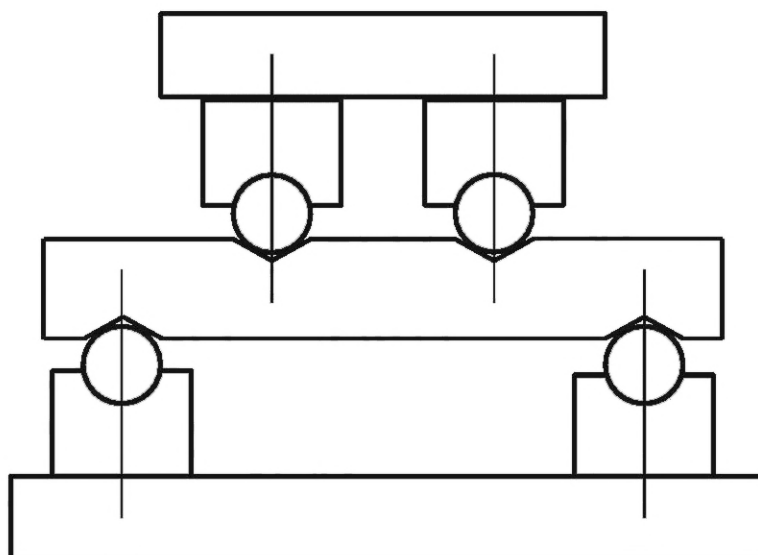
Установочный блок с канавками для позиционирования роликов
